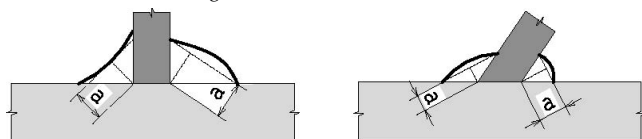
Definizione dell'area di gola per le saldature a cordone d'angolo
